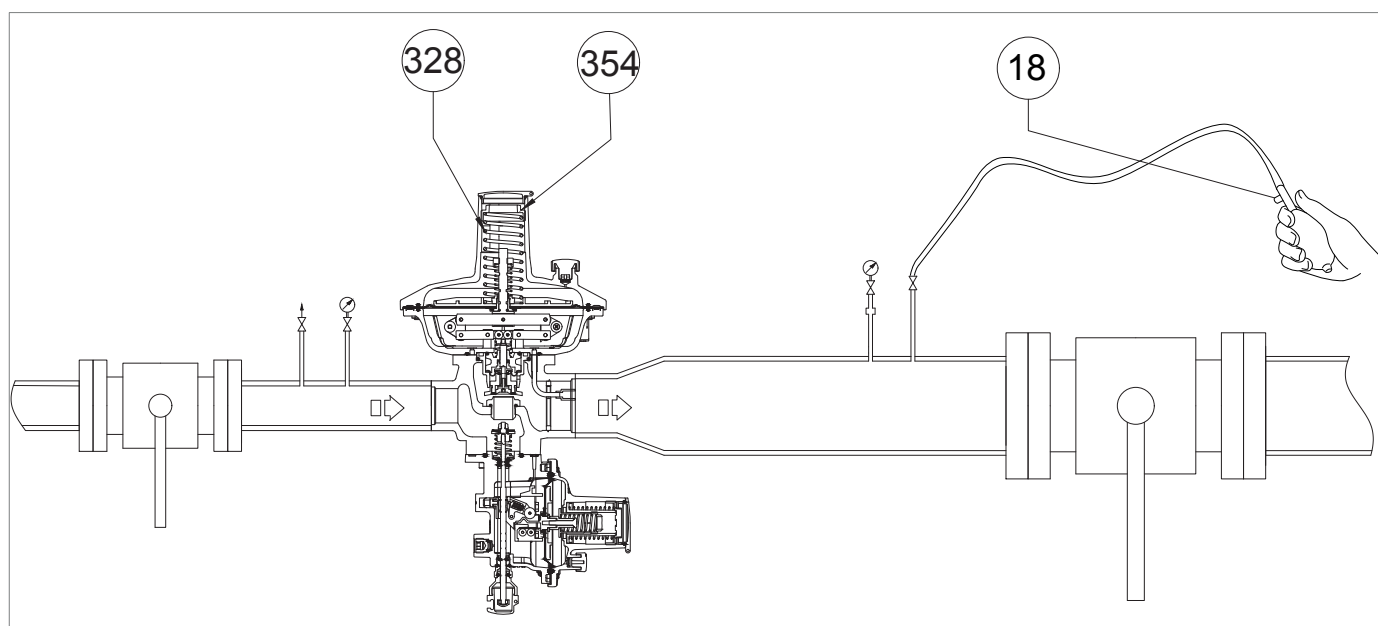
Druckbeaufschlagung mit externer Quelle für eingebautes Absperrventil LA
